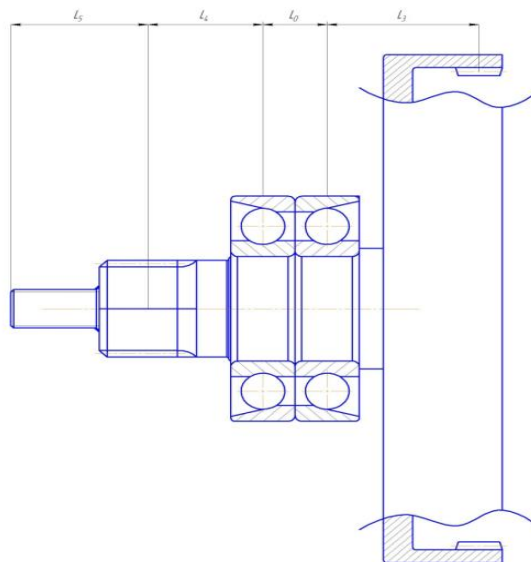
Конструкция ведомого вала колесного редуктора
